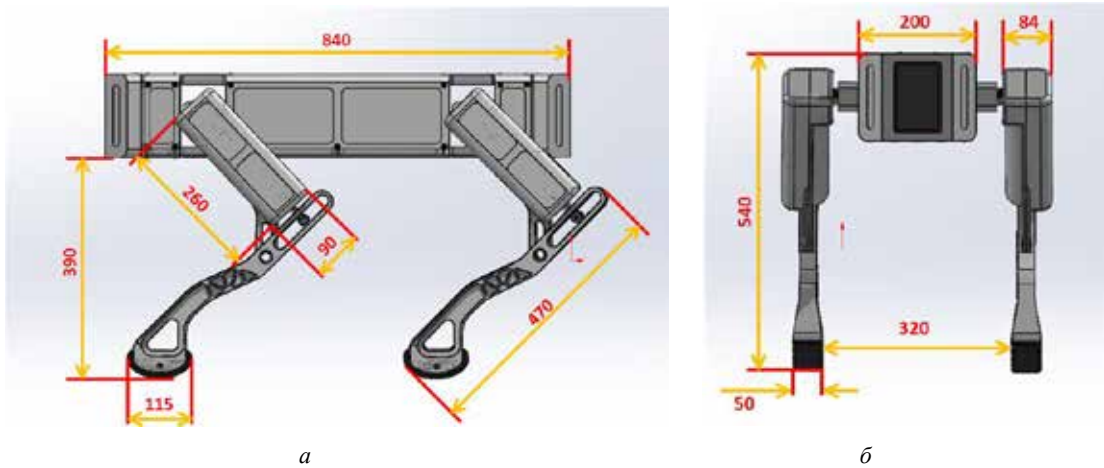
Модель прототипу конструкції: а – вид збоку, б – вид спереду
